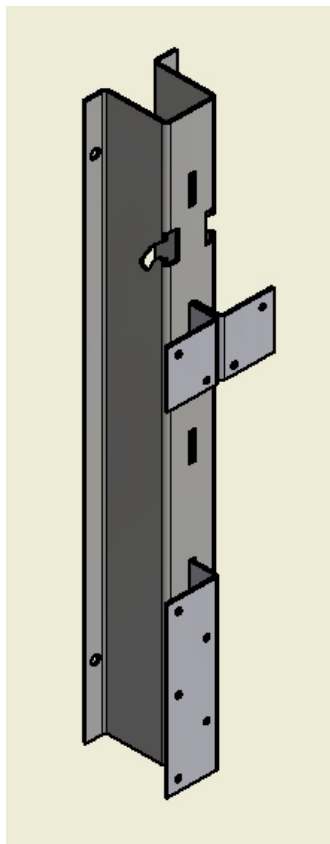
Cartola com os componentes para suportar equipamentos ligados por encaixe removível.
